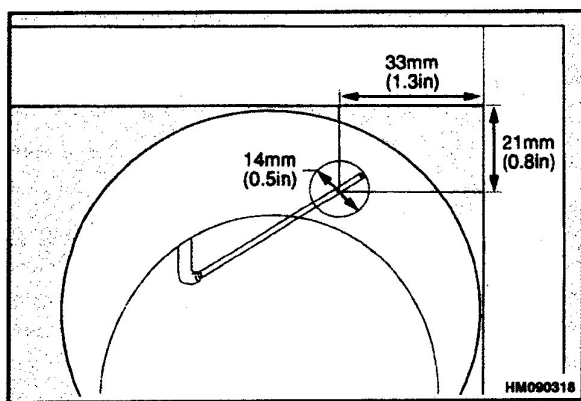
Регулировка сопла охлаждения поршня, двигателя типа YG и YH
